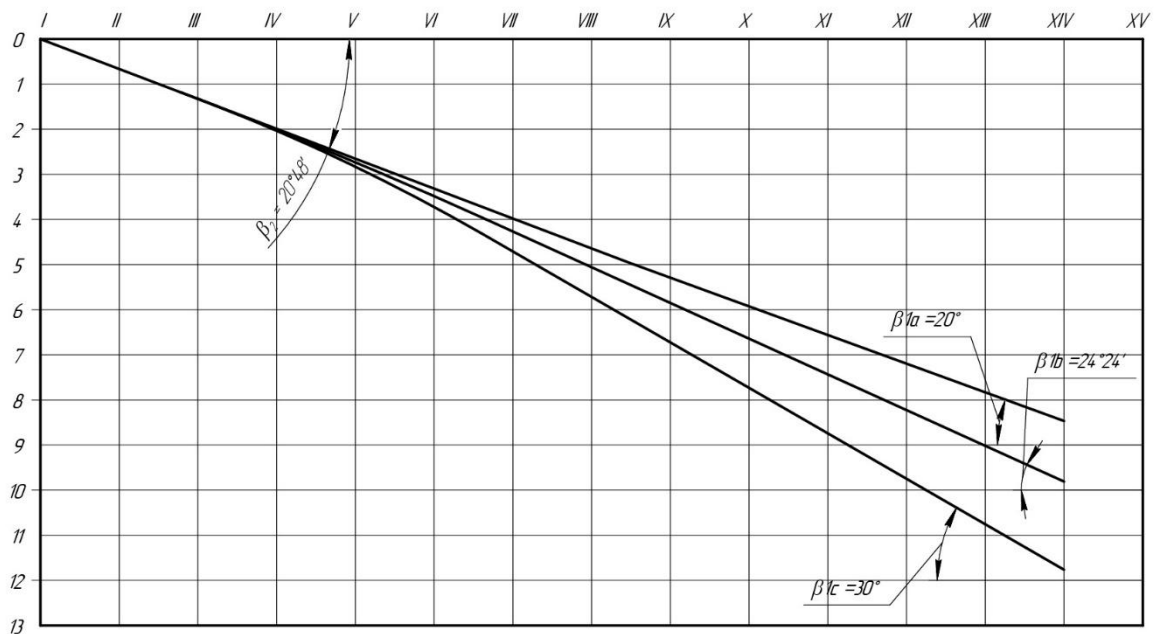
Профілювання поверхні лопаті на розгортці циліндра
